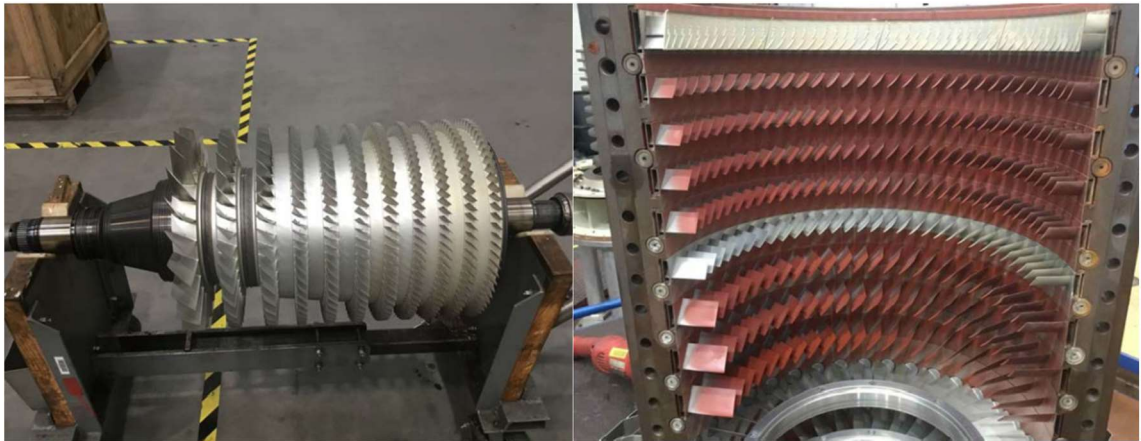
Schéma de rotor et stator du Compresseur axial
